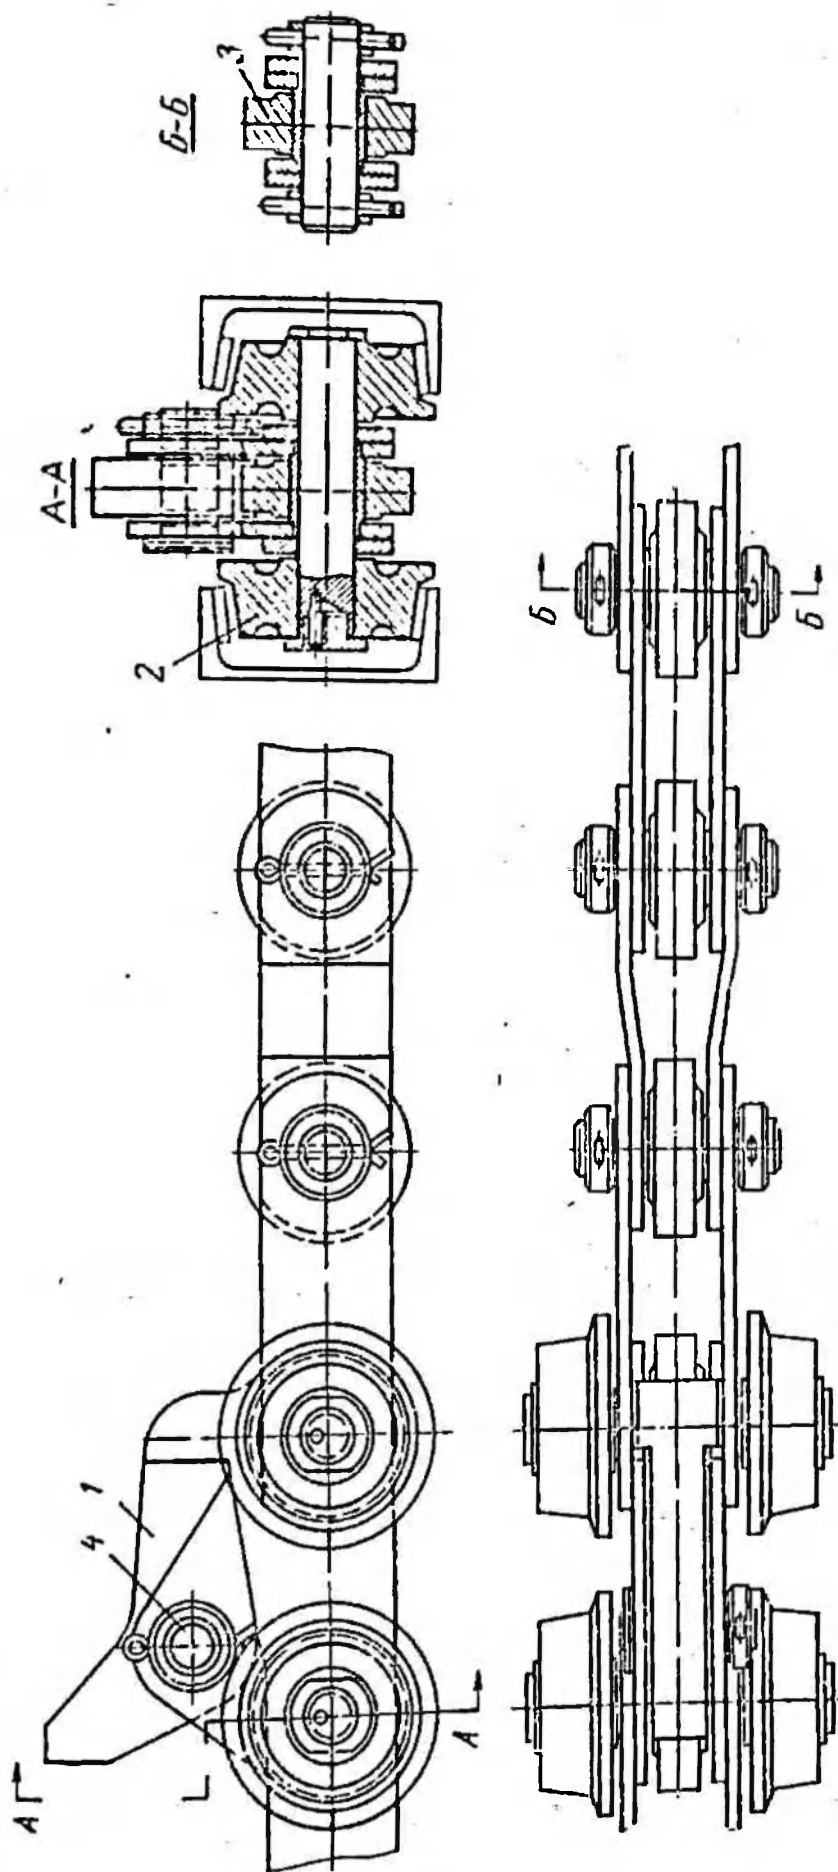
Детали рабочей цепи толкателя ПЭТ-3
